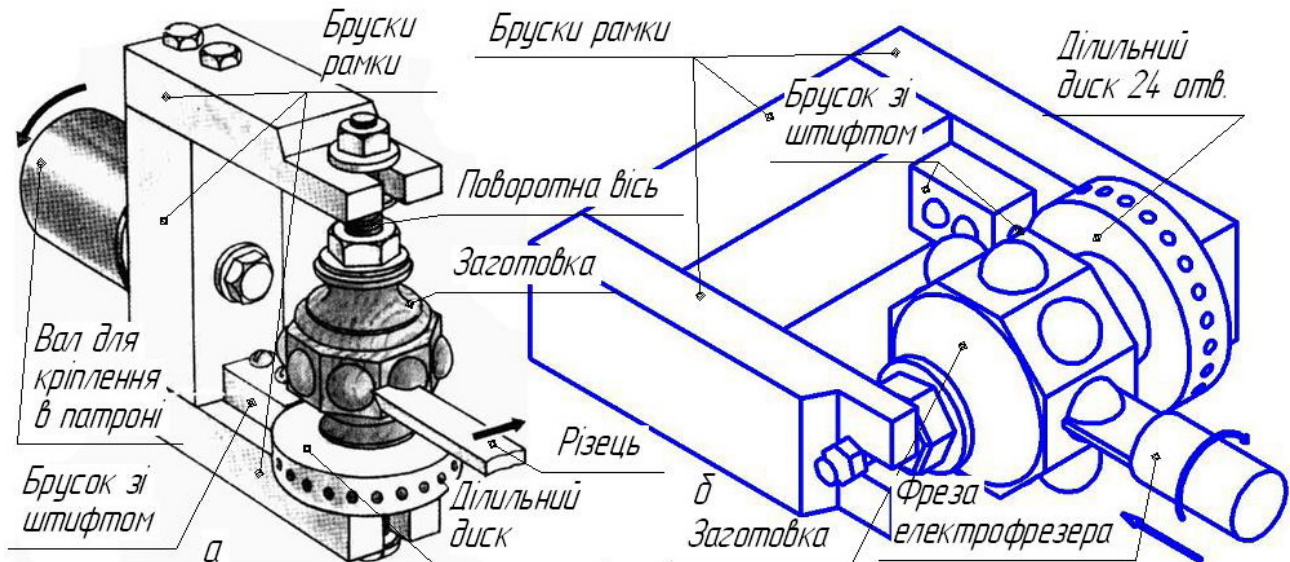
Принципові схеми пристрою для точіння (а) і верстата для фрезерування деталей з кількома осями обробки (б)
